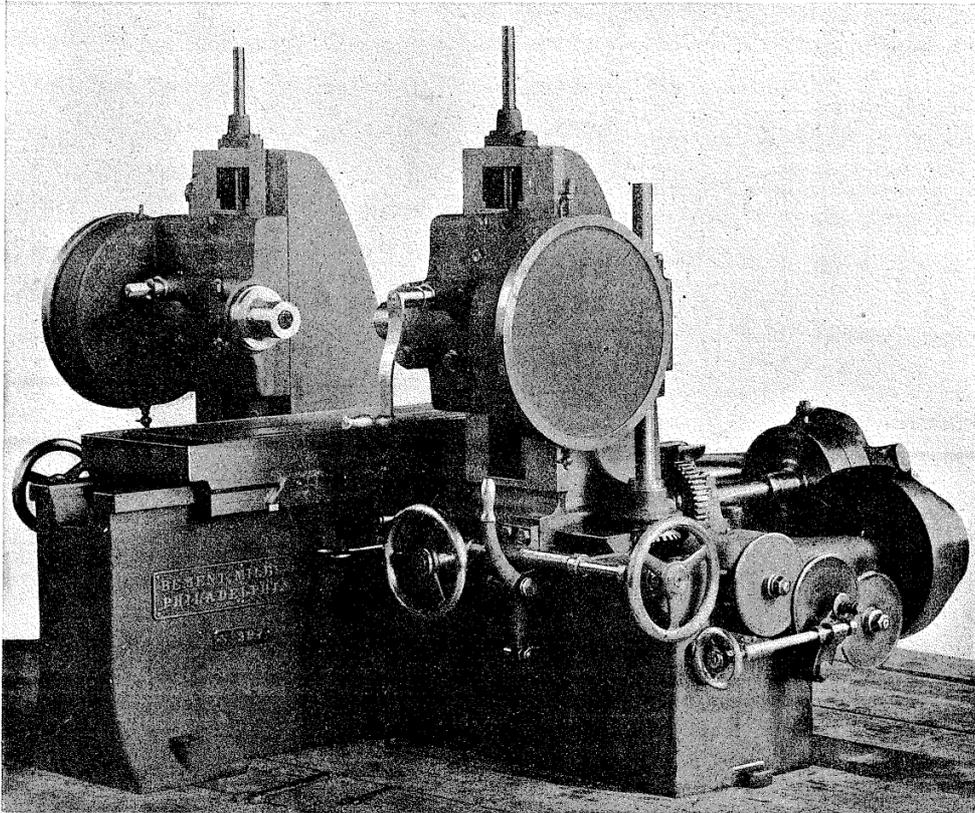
Fraiseuse raboteuse *Bement Miles*, écartement des montants 585 à 1^m,10, entre les broches 300 à 810, de la table à l'axe des broches 75 à 460, broches de 100 millimètres, équilibrées indépendantes, avancées par friction de 0^{mm},8 à 8 millimètres par tour de la fraise, ou de 25 à 230 millimètres par minute.
